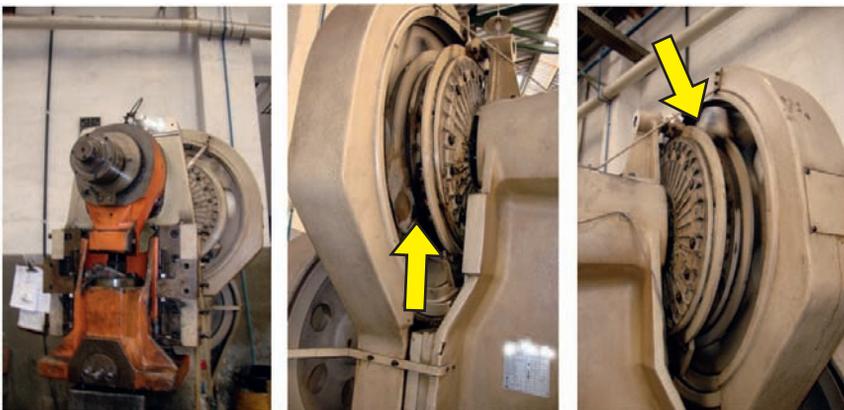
Prensa mecânica excêntrica freio/embreagem montada em estrutura de prensa mecânica excêntrica de engate por chaveta.
